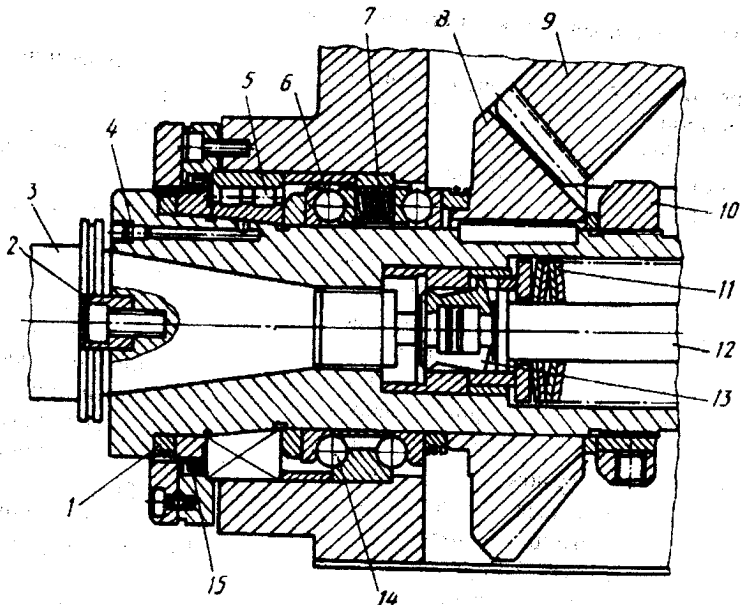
Передня опора та кінець шпинделя фрезерно-розточувального верстата з ЧПК
